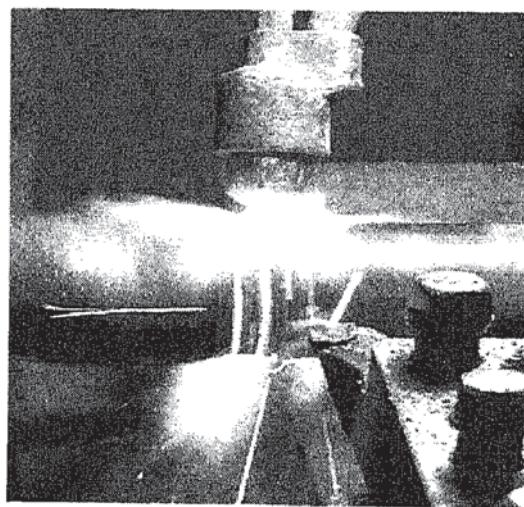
Фотография резания с нагревом цилиндрической заготовки из стали 45
